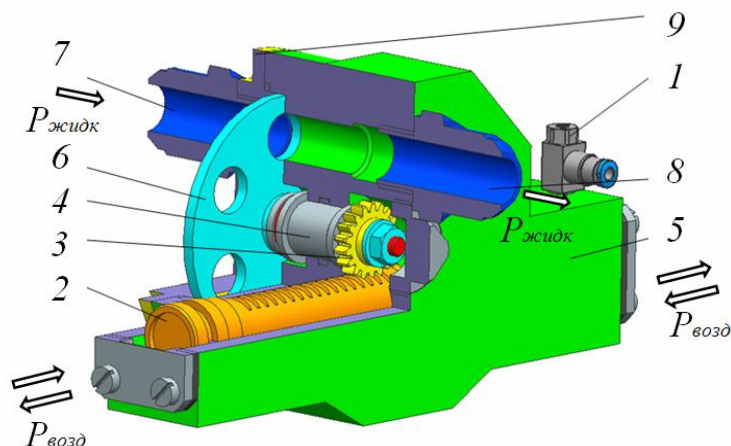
Конструктивная схема гидромеханического генератора колебаний: 1 – дроссель; 2 – рейка-шток; 3 – шестерня; 4 – вал; 5 – корпус; 6 – перфорированный диск; 7,8 – штуцеры подвода и отвода жидкости; 9 – крышка
